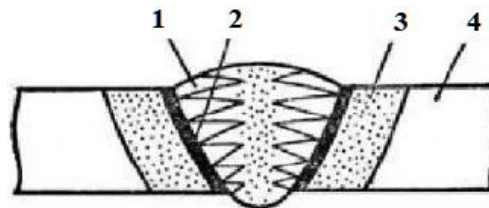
Различные зоны металла в сварном соединении: 1 – сварной шов; 2 – зона сплавления; 3 – зона термического влияния (околошовная зона); 4 – основной металл
